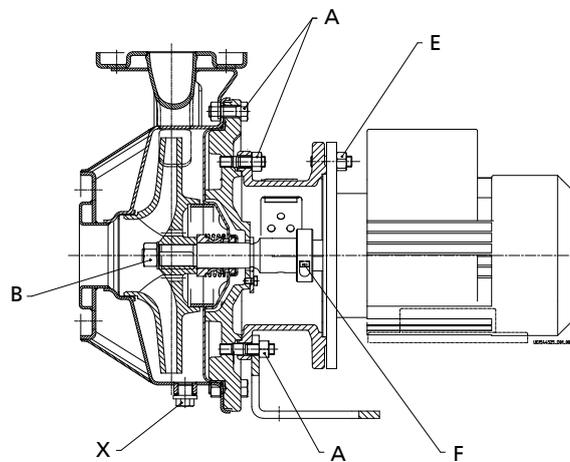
Schraubenanzugstellen für Etachrom B 050-025-250, 050-032-250, 065-040-250, 065-050-200, 065-050-250, 080-065-200, 080-065-250, 100-080-200, 100-080-250
